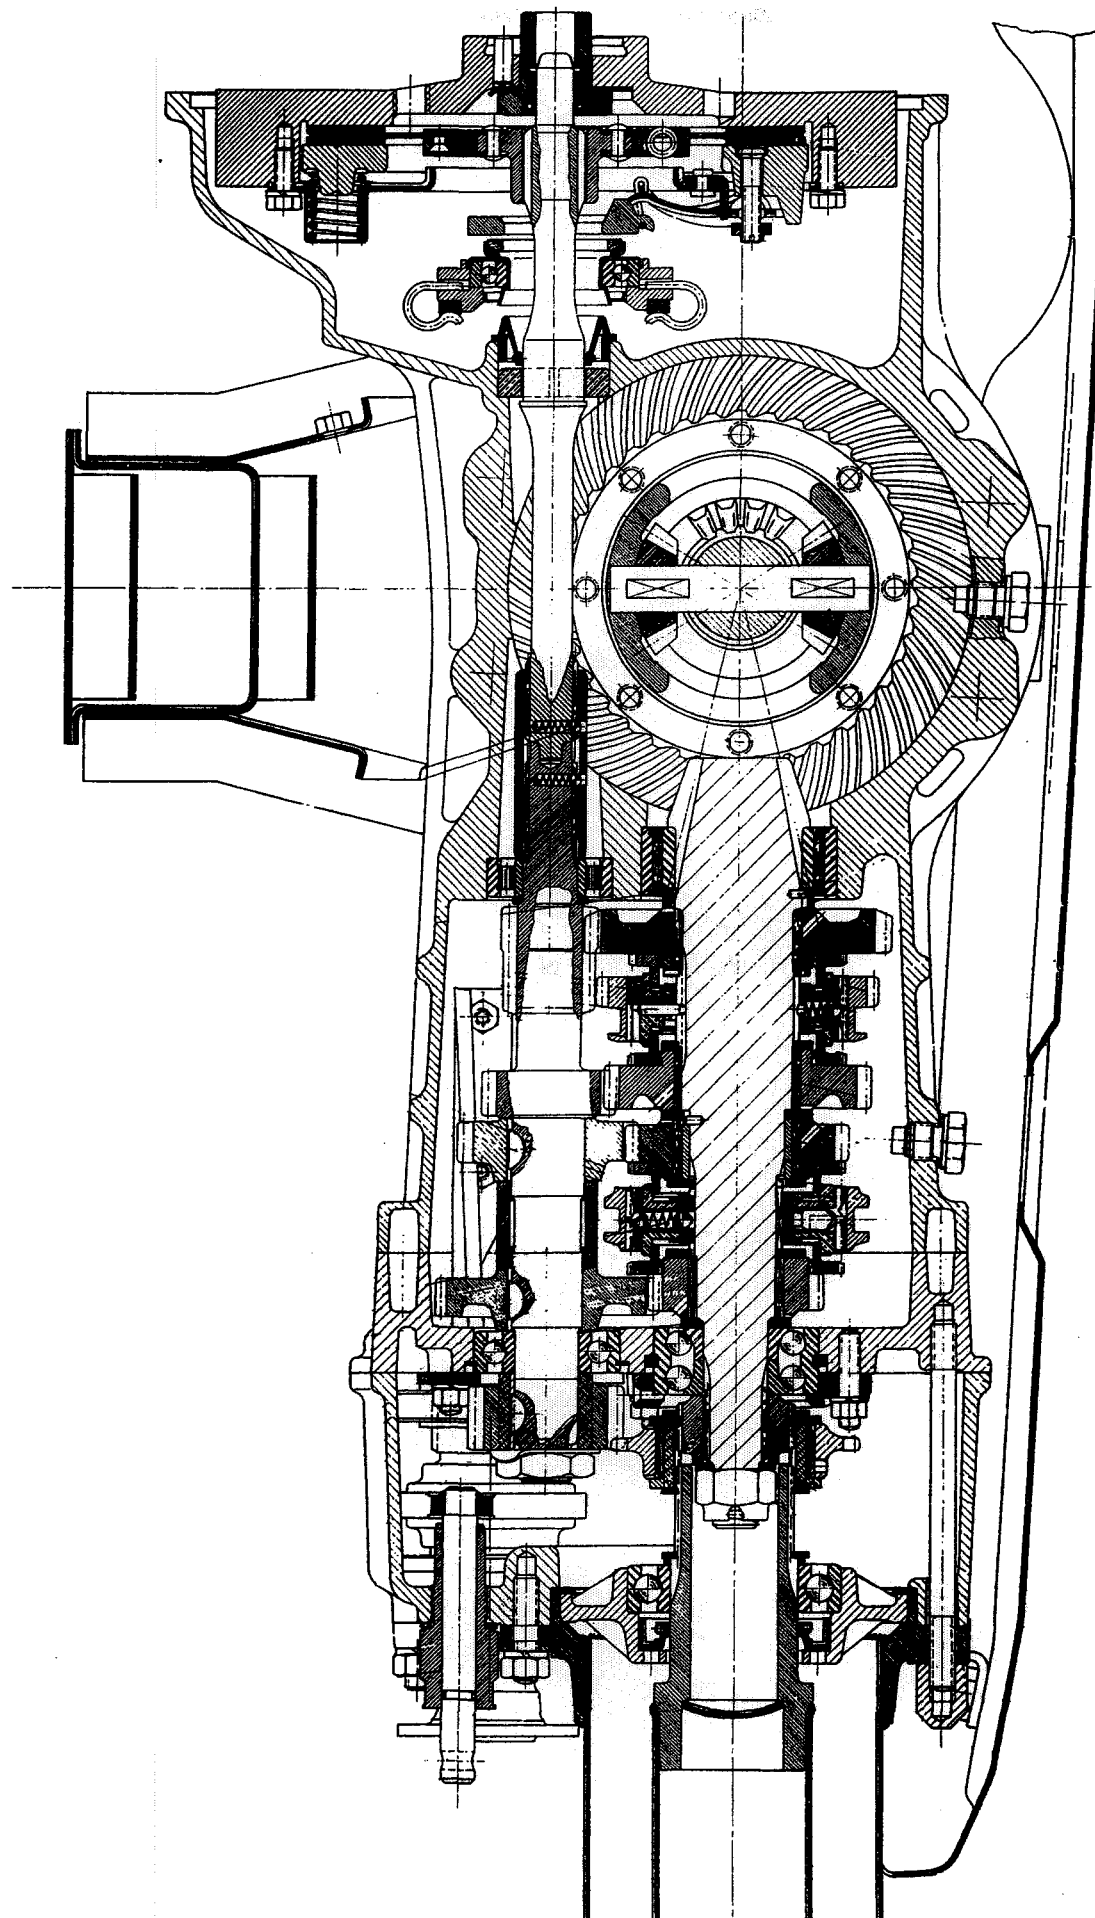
/I: Getriebe - Gear - Engrenage de transmission
